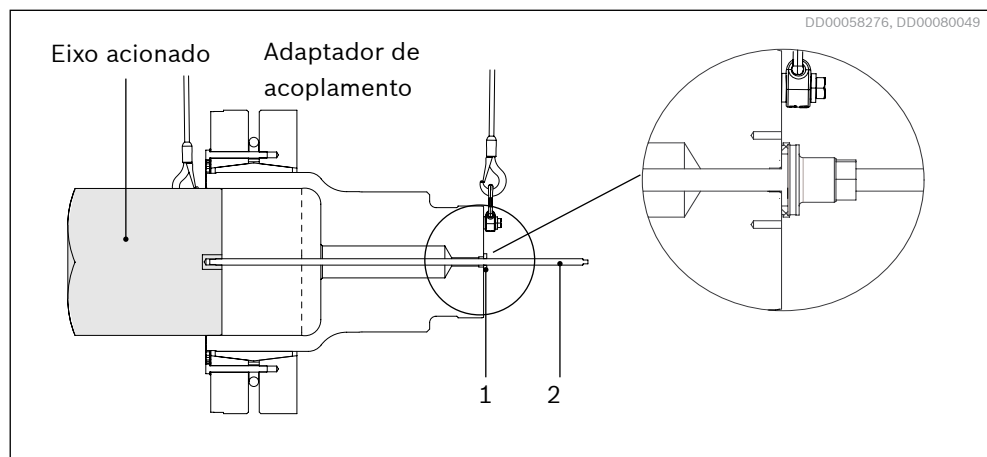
Montagem do adaptador de acoplamento no eixo acionado com a ferramenta de montagem.
